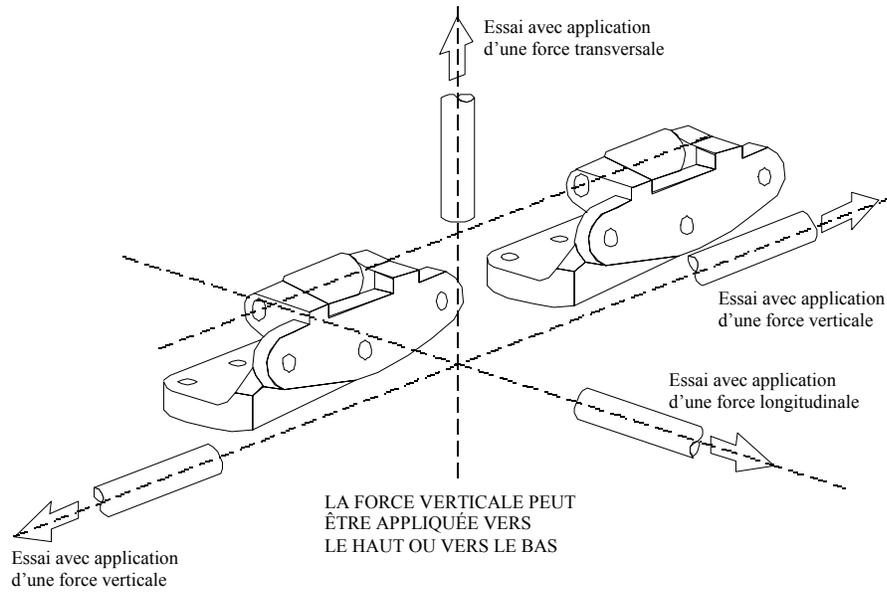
Directions d'application des forces lors des essais statiques sur les portes arrière
